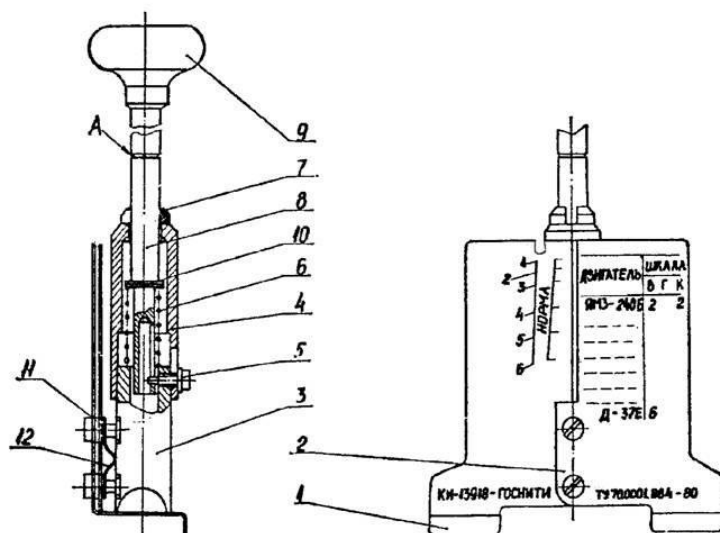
Пристосування КИ-13918-ГосНИТИ для перевірки і регулювання натягу пасу приводу компресора пневматичної системи:
